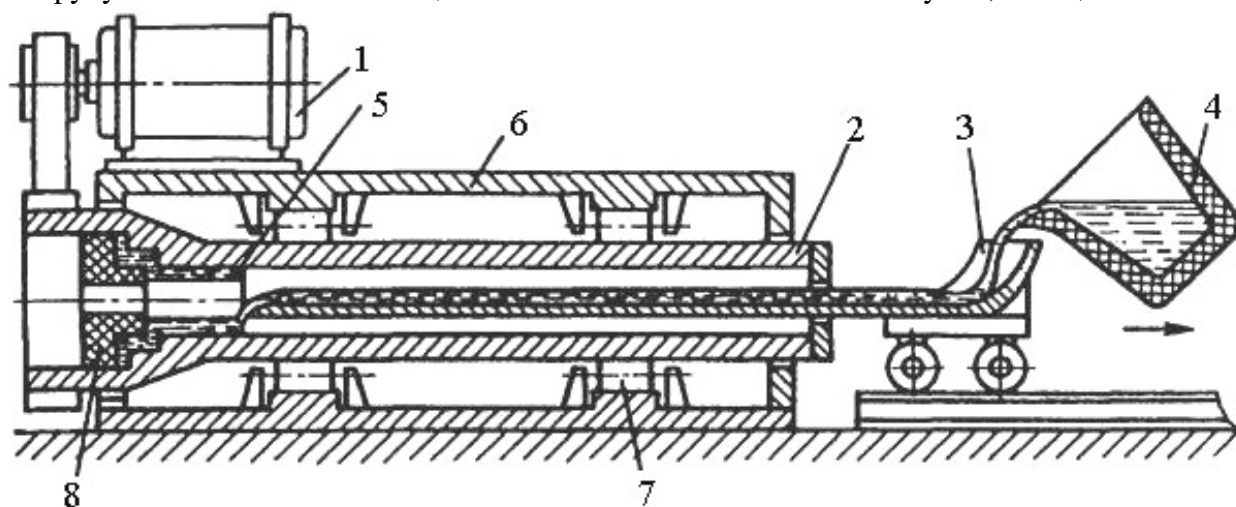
Схемы процессов изготовления отливок центробежным литьем:
